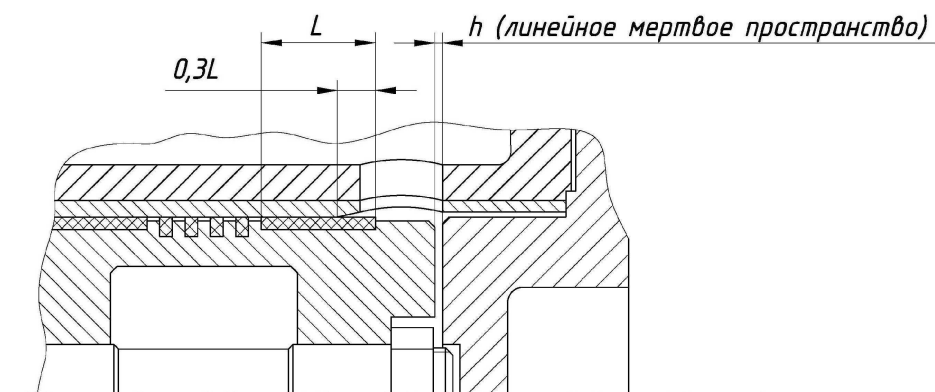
Схема перебега направляющего кольца с рабочей поверхности цилиндра
